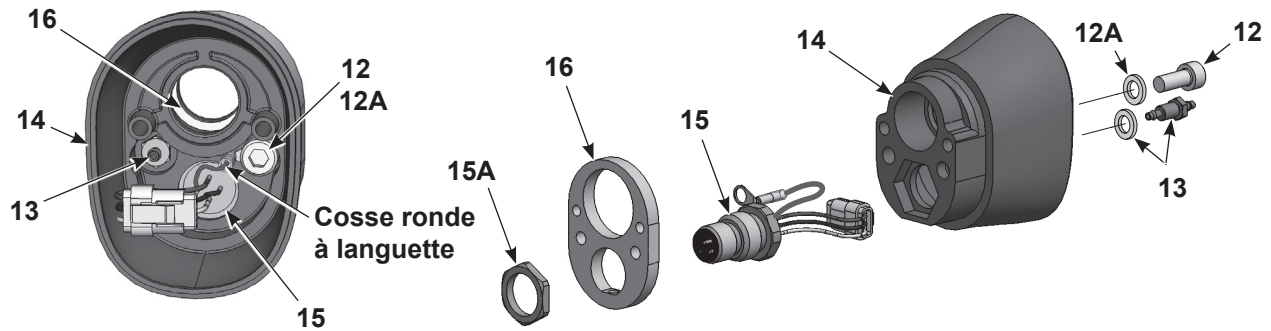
Démontage du pistolet à fixation sur tube 5 sur 5
